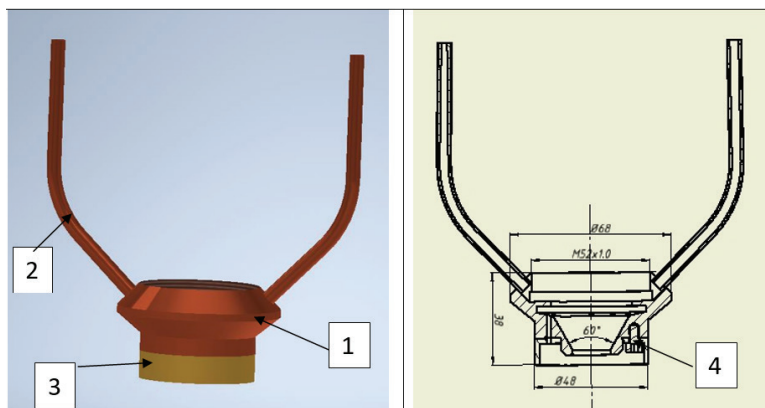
Загальний вигляд та поперечний розріз сопла для подачі захисного газу: 1 – сопло захисного газу; 2 – трубки подачі порошку; 3 – ковпак захисний; 4 – гвинт фіксації захисного ковпака
